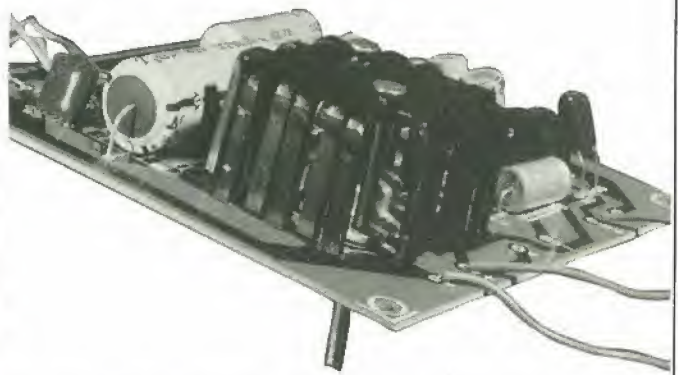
Lo stesso oggetto misterioso visto da Sud-Ovest.
